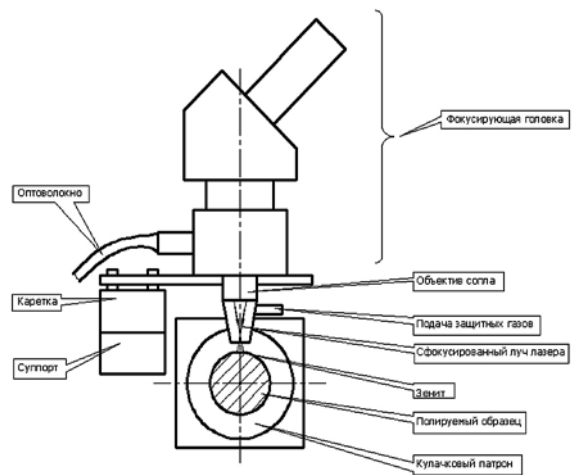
Схема наладки токарного станка для операции лазерно-плазменного полирования
